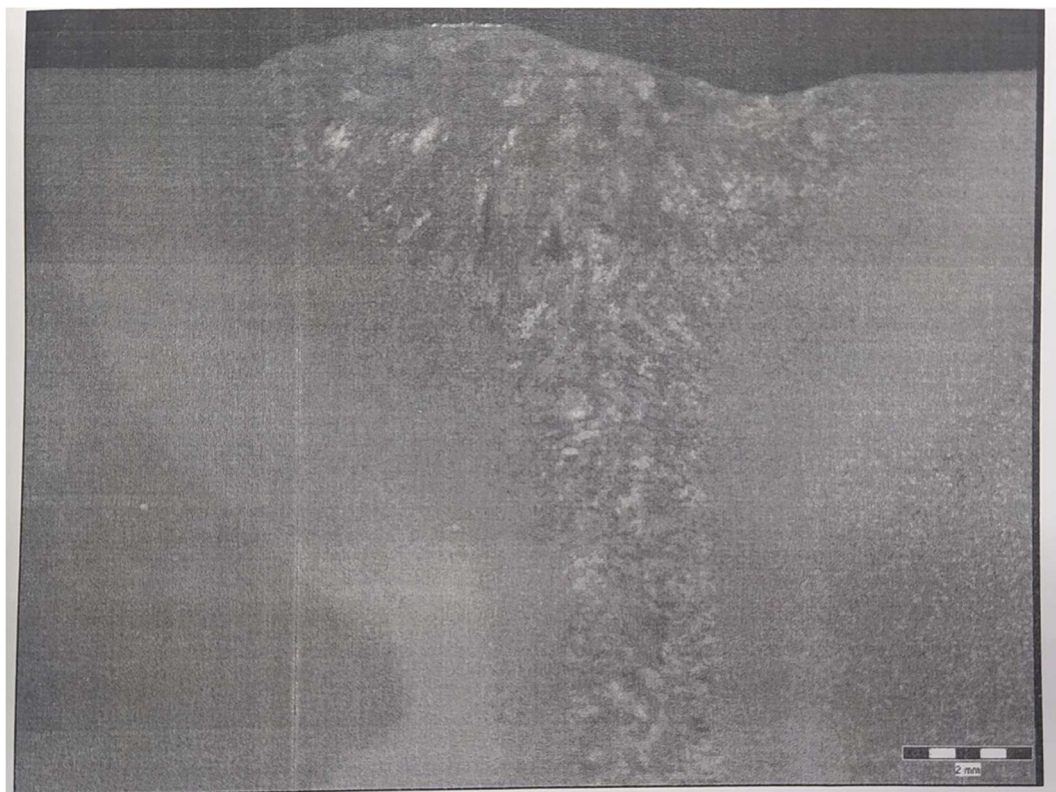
Макроструктура зварного шву зразка ЗСЗ
